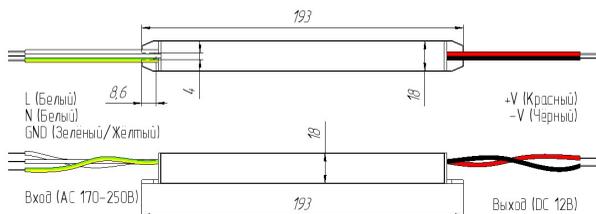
Габаритные размеры блока питания Geniled GL-12V24WM20 Slim.
